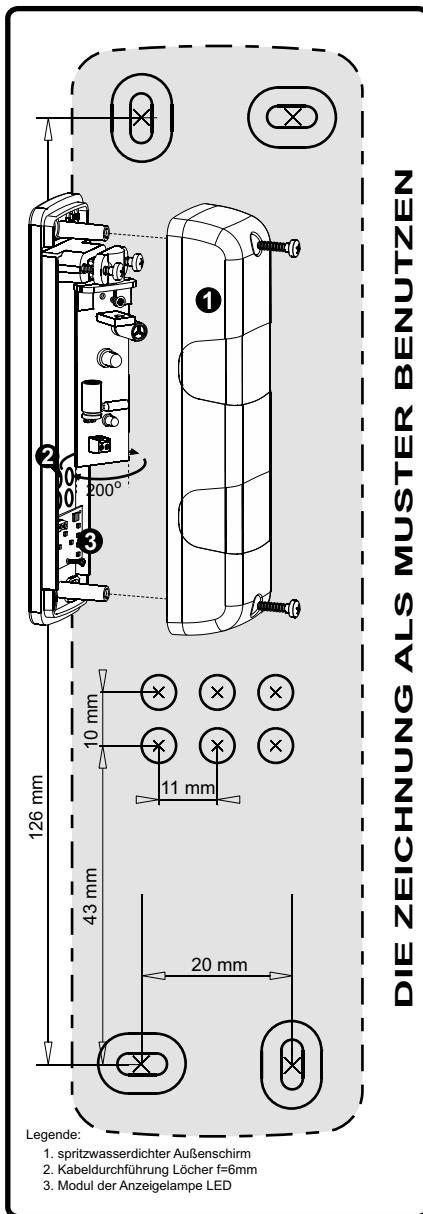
Das Bohrlochbild für Montage im Maßstab 1:1 mit Zusammenstellungszeichnung.
